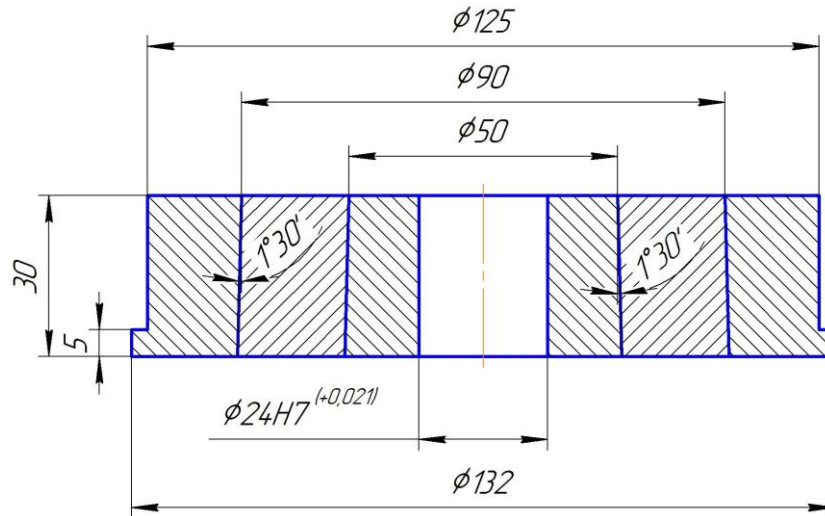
Двобандажована матриця для зворотного холодного видавлювання деталі «Втулка».
